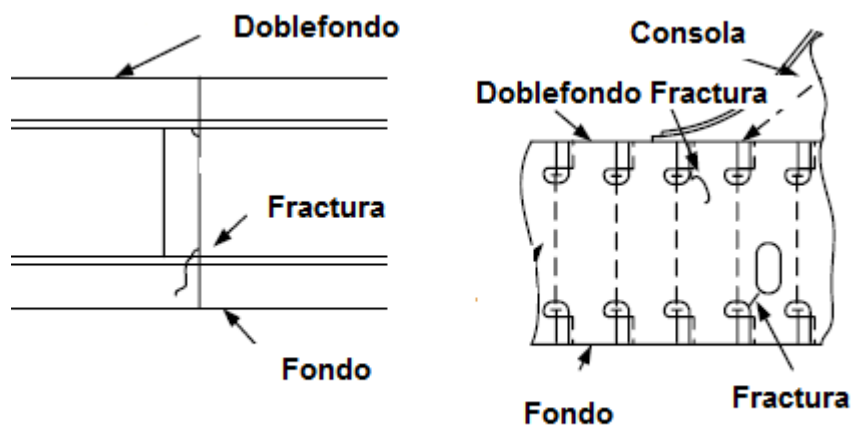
Ejemplos de rotura en la zona entre el fondo y el doblefondo
